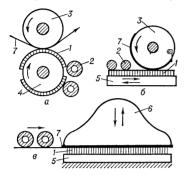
Схемы построения печатных аппаратов: a — ротационный; 6 — плоскопечатный; a — тигельный; 1 — печатная форма; 2 — накатные валики красочного форма, 2— накатыре балып красот, аппарата; 3— печатыр цилиндр; формный цилиндр; 5— талер; 6— гель; 7— бумага.
